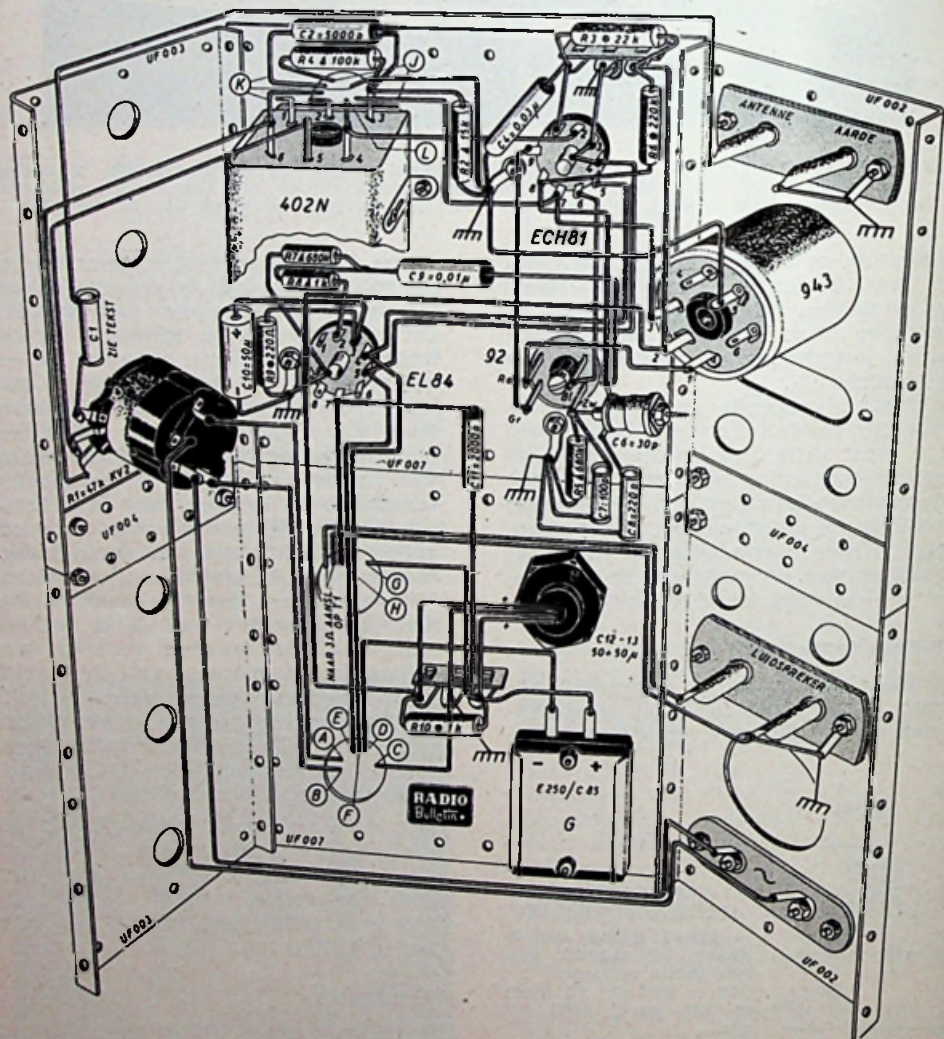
MONTAGEPLAN VAN DE UN-44
